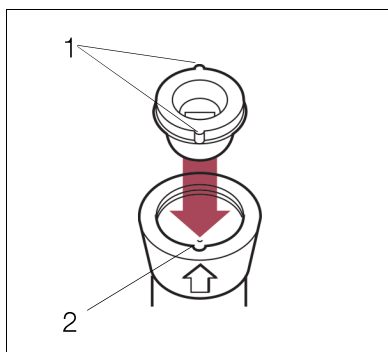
Einsetzen des Sensors mit dem optionalen Spreizwerkzeug
